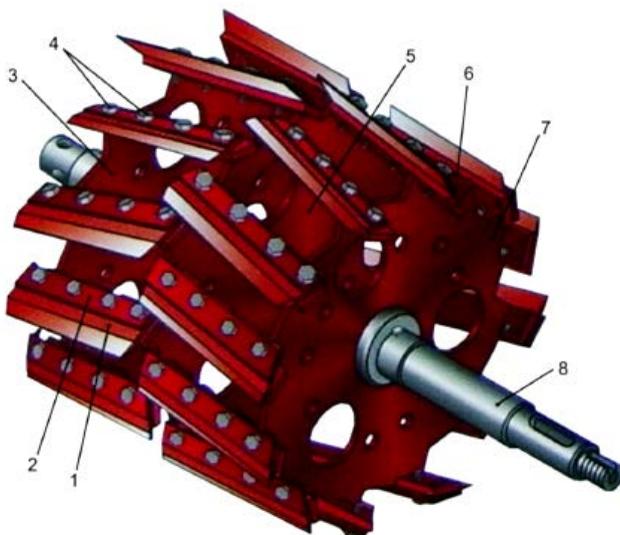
Измельчающий барабан (шевронного типа): 1 – нож; 2 – прижим ножа; 3, 7 – диски крайние каркаса барабана; 4 – болты крепления ножей; 5 – диск средний каркаса барабана; 6 – опора ножа; 8 – вал барабана
